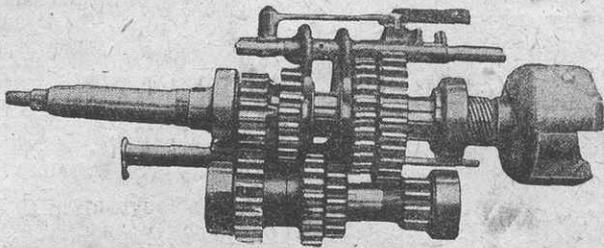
Механизм коробки передач компрессорного автомобиля «Мерседес-Бенц» (вид с левой стороны, считая по направлению движения).
